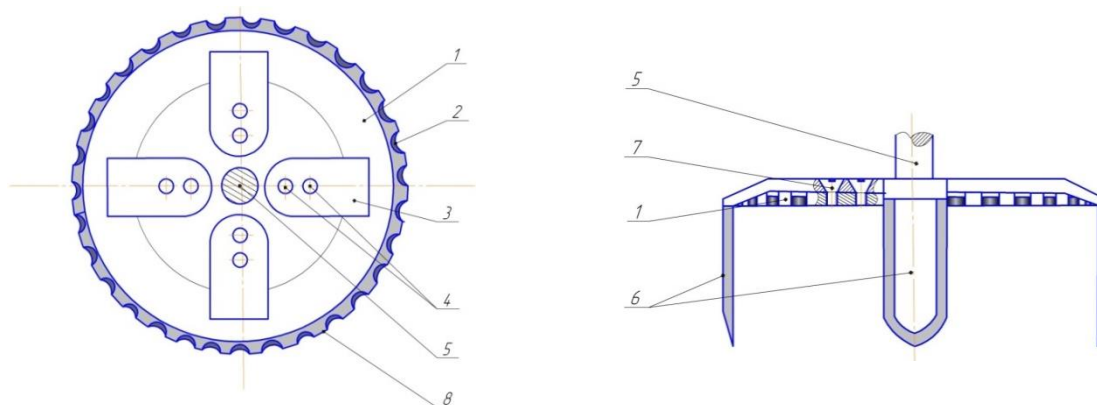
Фланец ротора фрезы с вертикальной осью вращения: 1 - фланец; 2 - серрийторная заточка; 3 – пазы; 4 – крепежные отверстия; 5 – вал; 6 – рабочий орган; 7 – крепежный винт; 8 – лезвийная часть;
